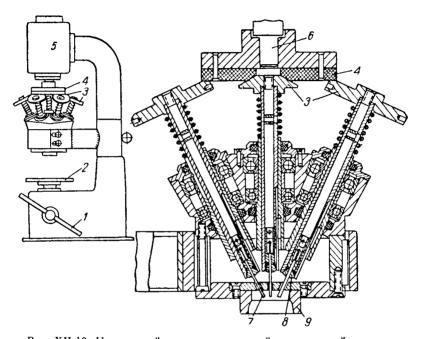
Настольный многошпиндельный сверлильный станок: 1— рукоятка; 2— стол; 3— ведомые диски; 4— резиновый диск; 5— электродвигатель; 6— хвостовик; 7— сверло; 8— цаиговый патрон; 9— гнездо кондуктора.
